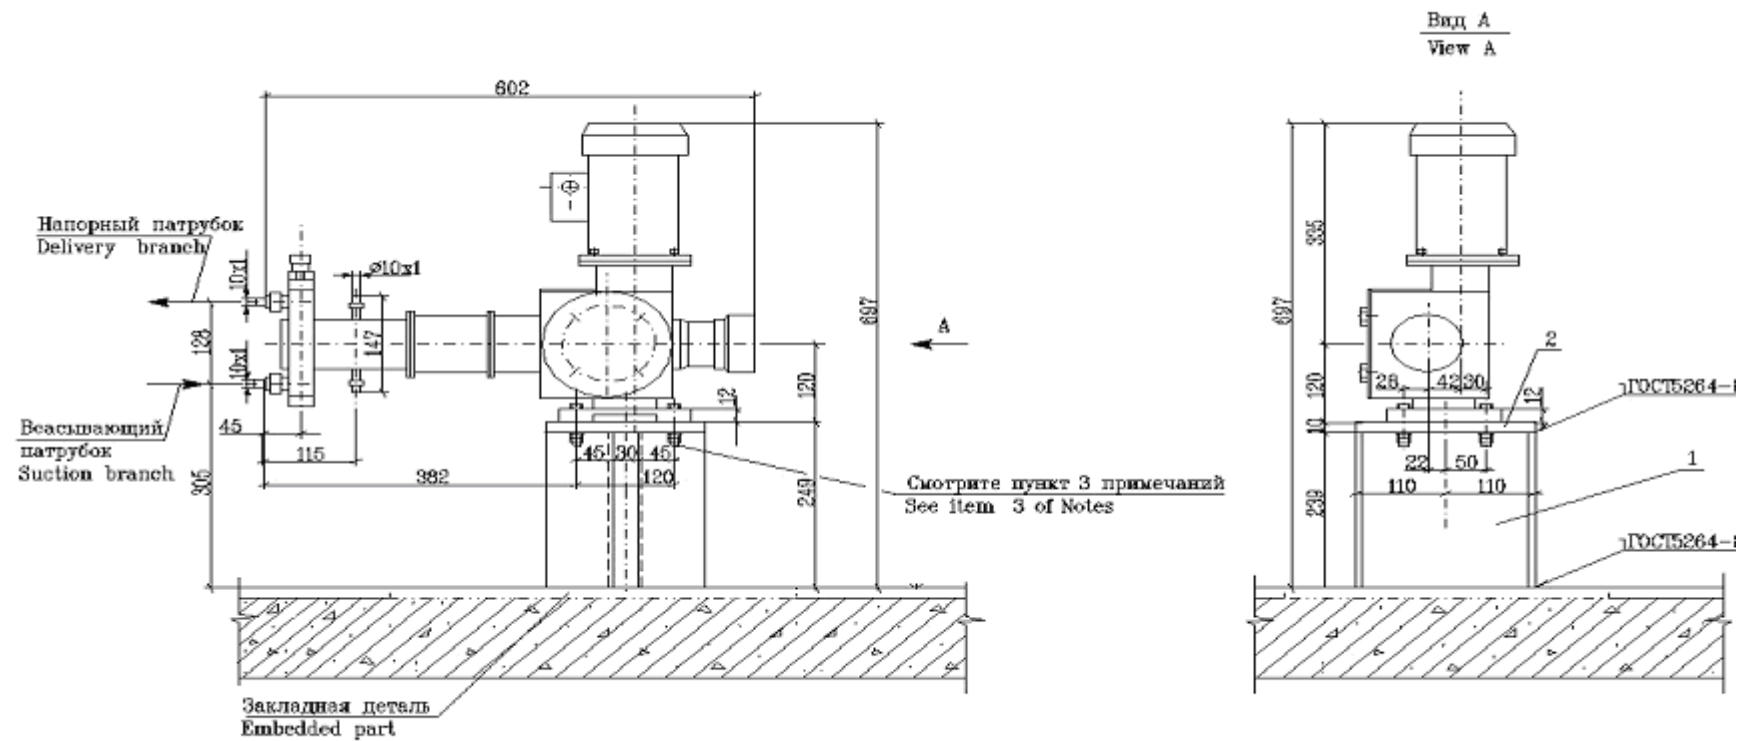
Габаритный чертеж насоса-дозатора LDN21AP001, LDN22AP001
